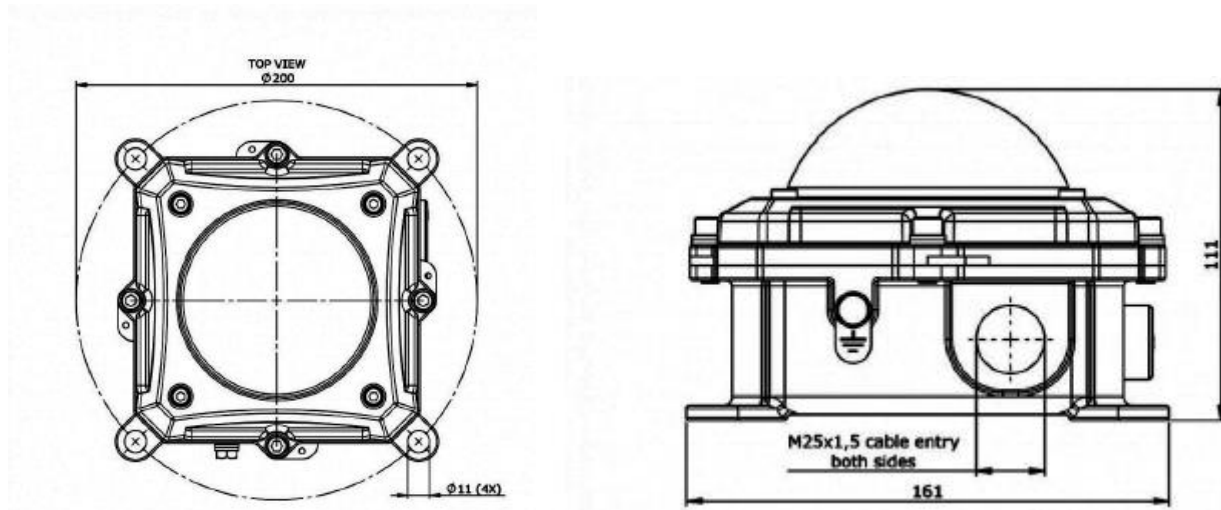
Planta y alzado de las luces perimetrales. Fuente: ORGA lighting.
